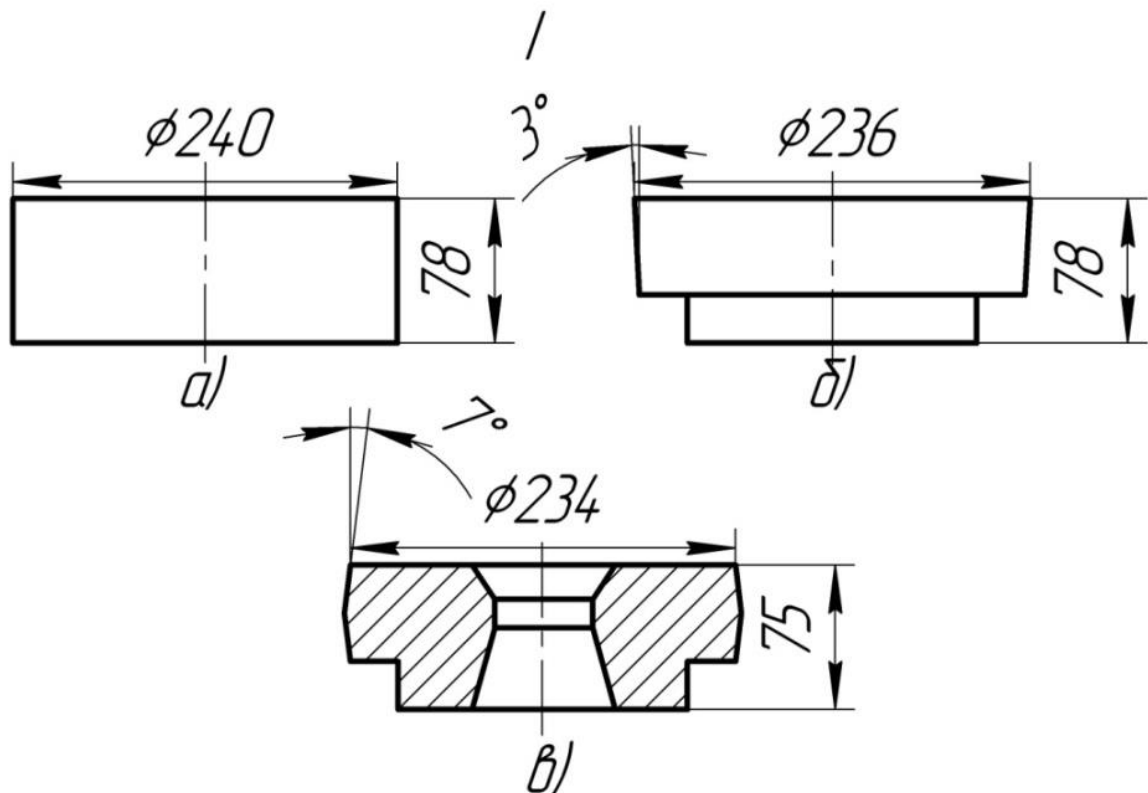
Ескізи заготовок: І – одновінцеві колеса;
